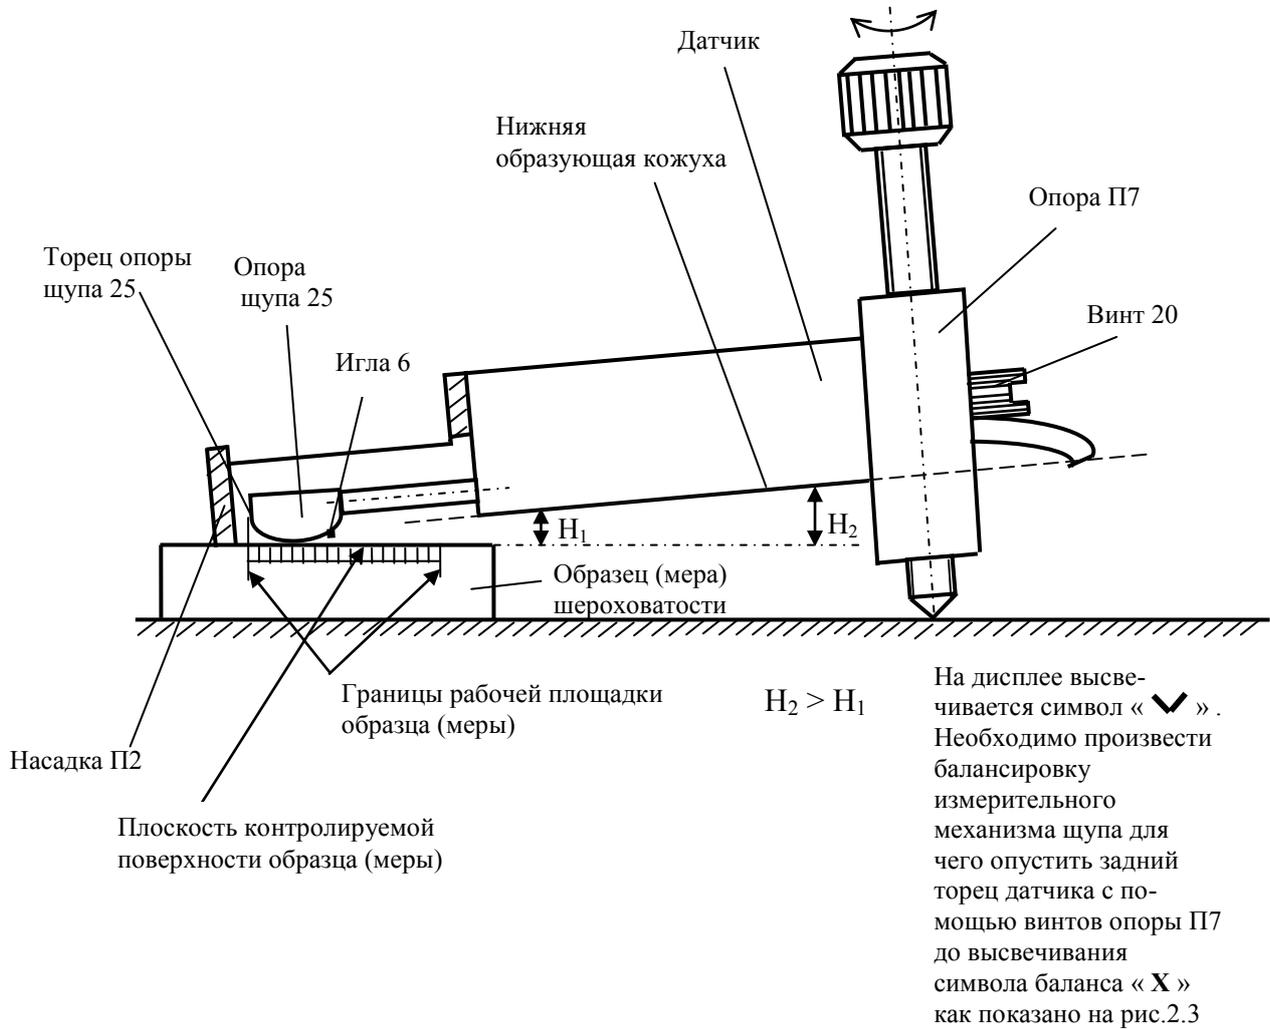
Базирование датчика на поверхность образца (меры) шероховатости с помощью опоры П7. Положение до начала балансировки. Вид сбоку.
